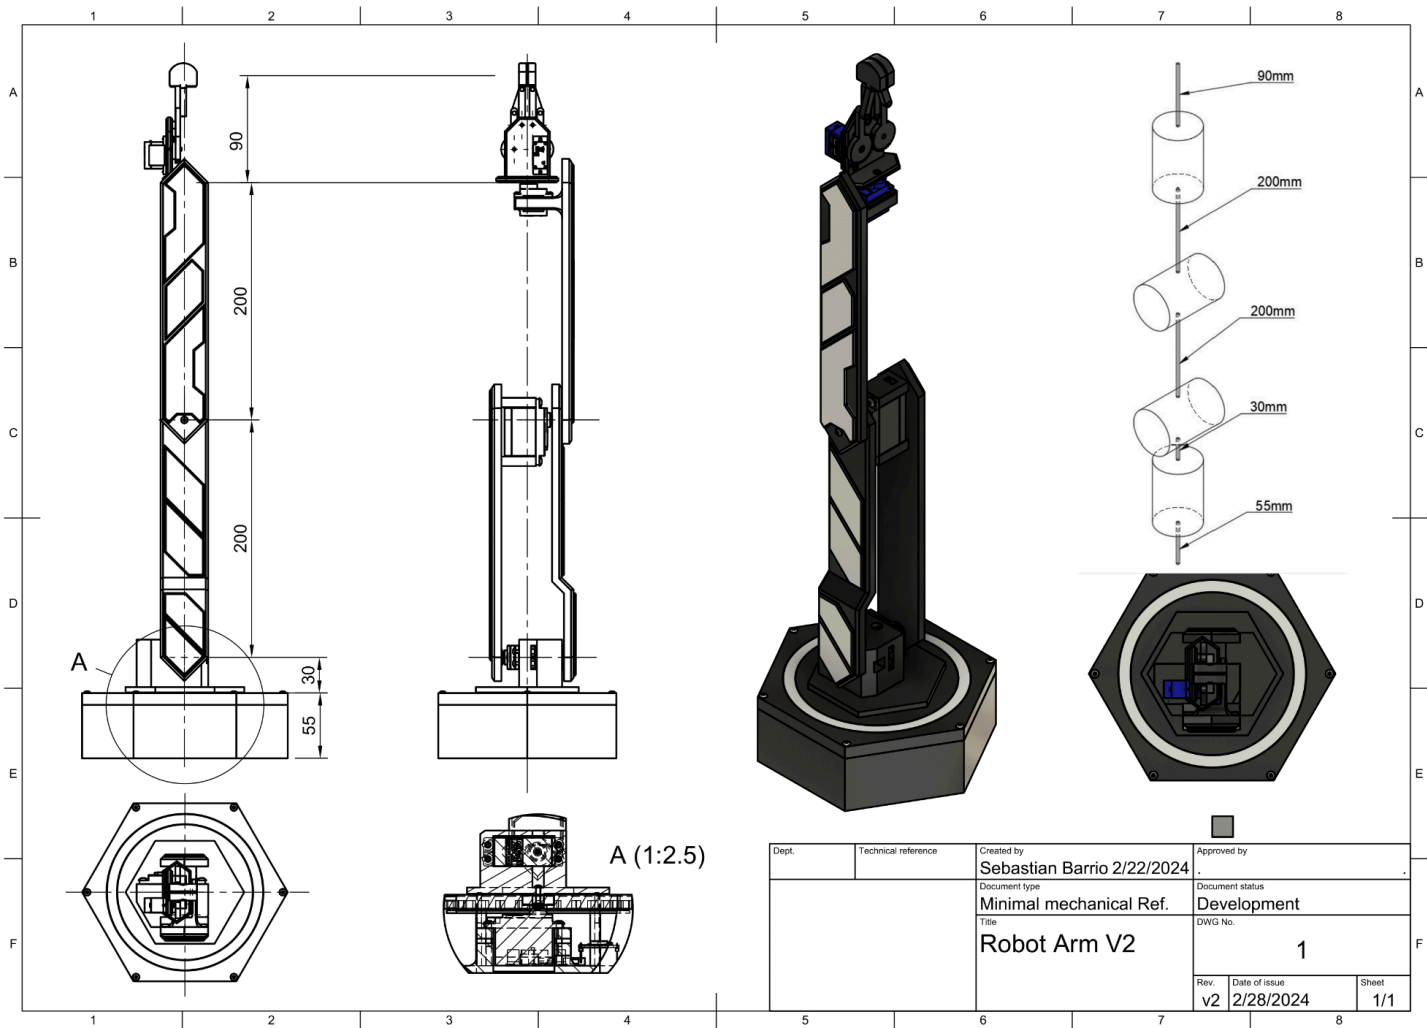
Dibujo técnico del cad, vista frontal, lateral, superior e isométrica, sección interna del servo de la base (A) y configuración cinemática ([link al cad](#))
